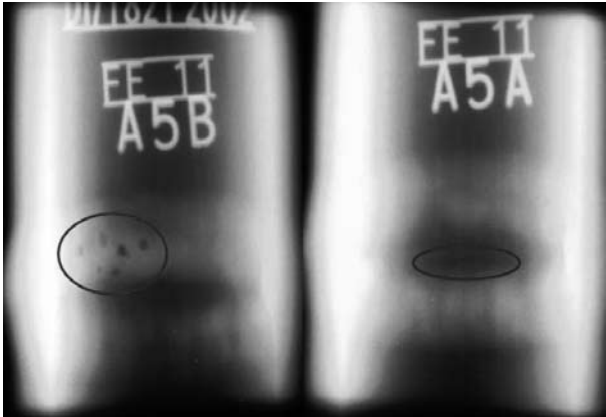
模拟缺陷试样 A5 焊缝底片影像
